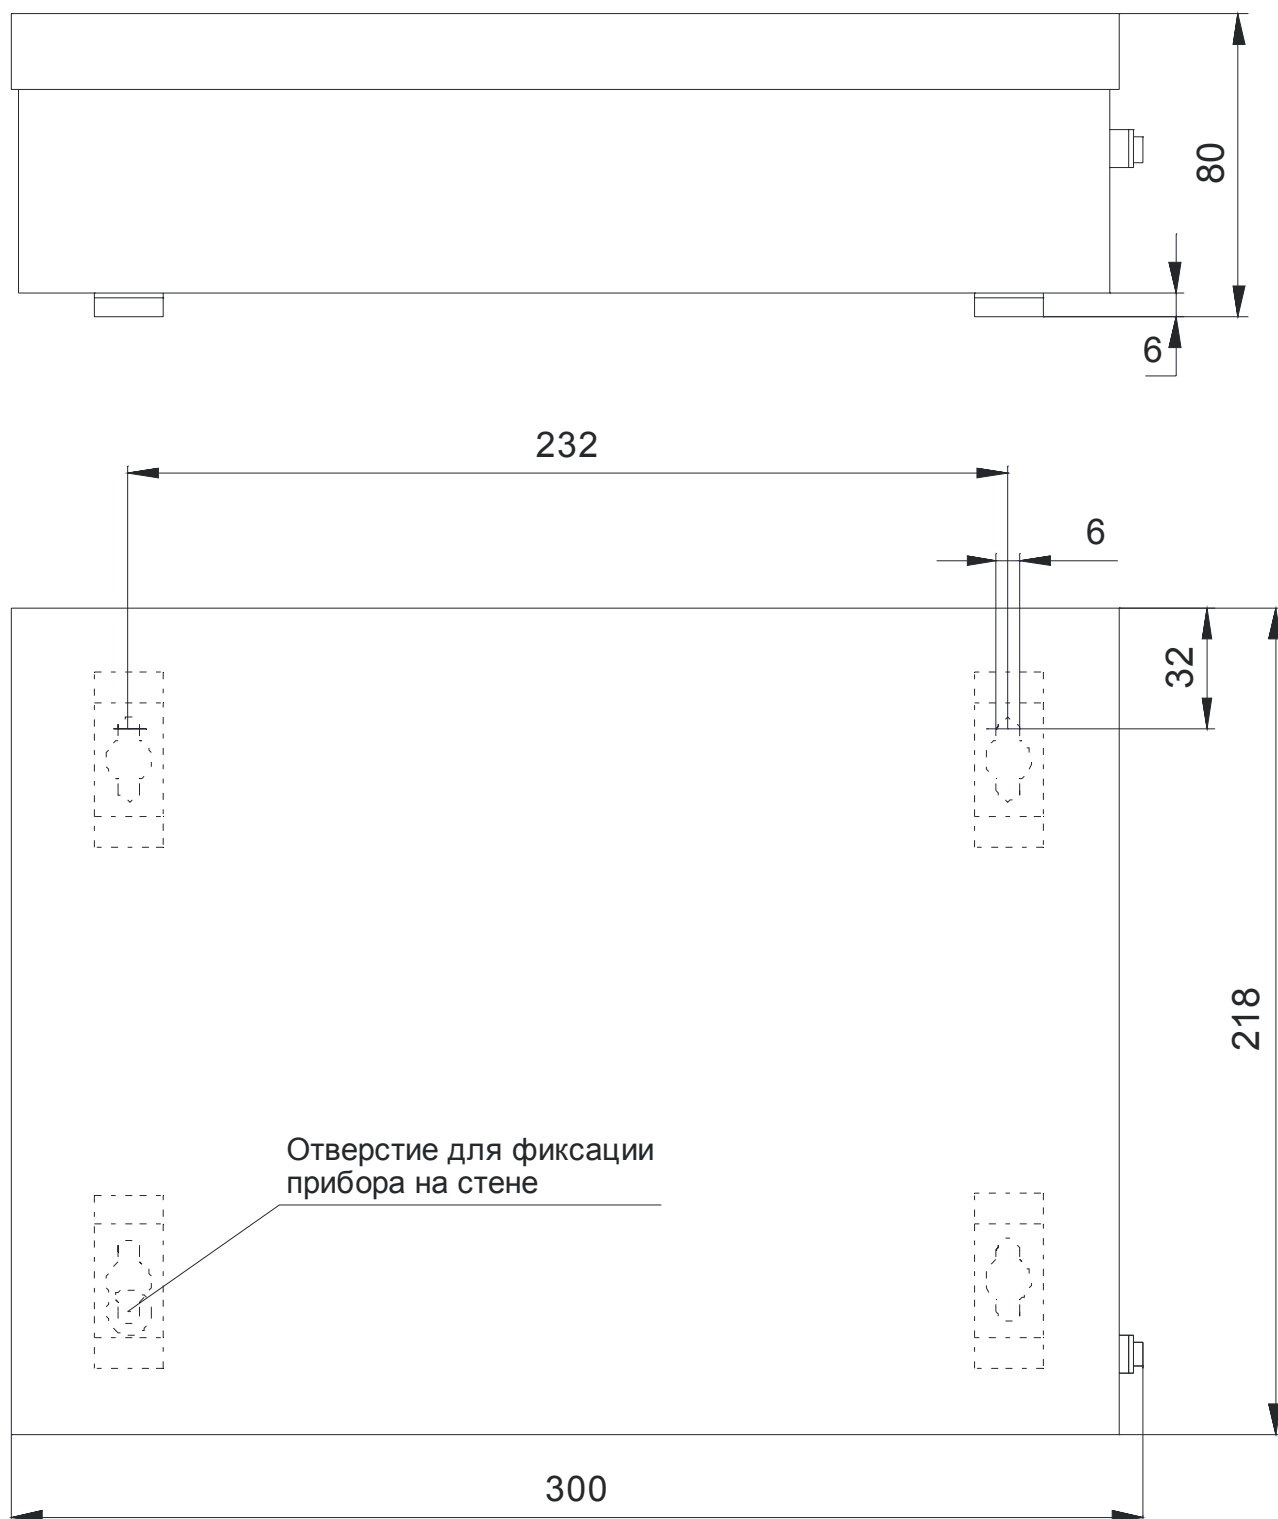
Габаритные и установочные размеры прибора ППКОП
